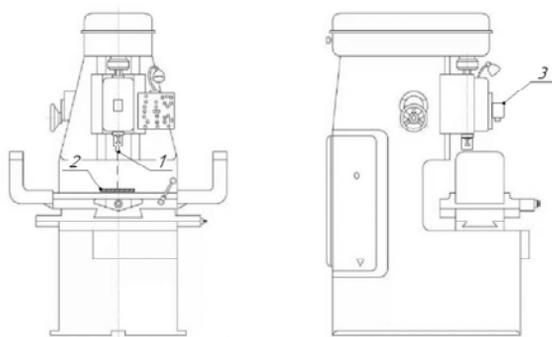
Схема установки системы бесконтактного измерения биения шпинделя на фрезерном станке
